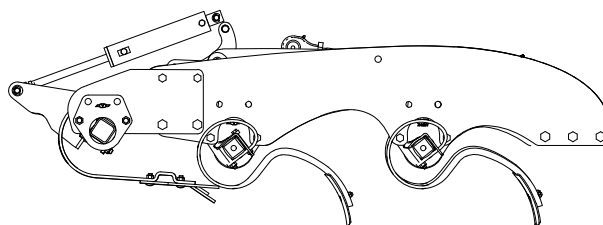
System Disc Aggressive CrossBoard Heavy
